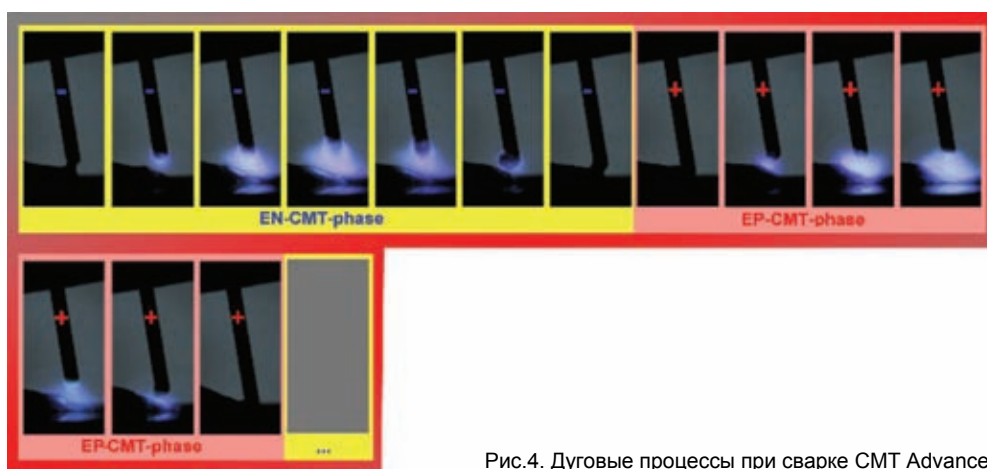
Дуговые процессы при сварке CMT Advance
